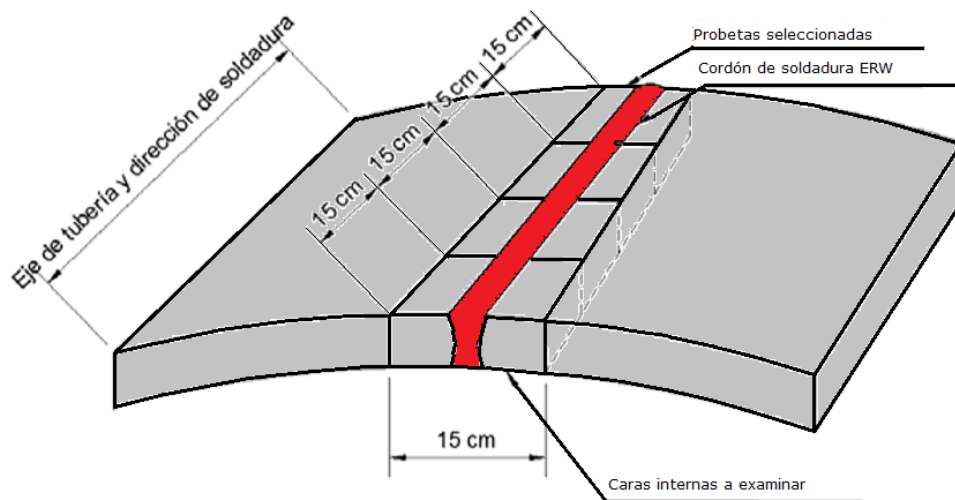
Distribución del corte para probetas con soldadura de resistencia eléctrica.
